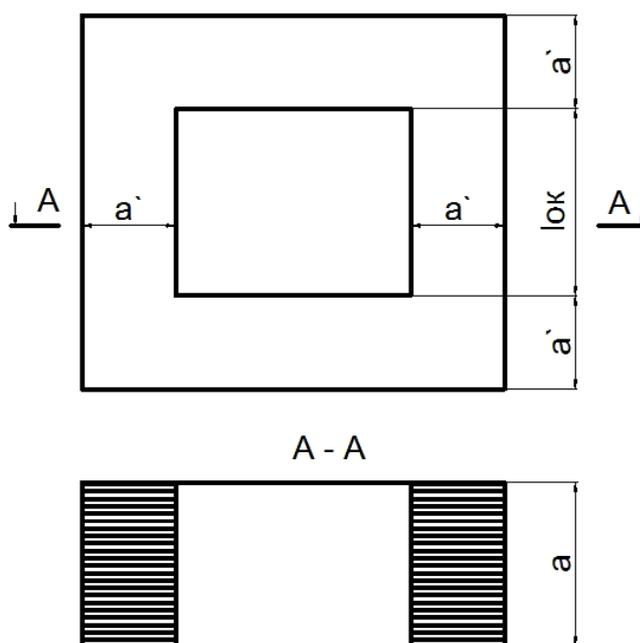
Магнитопровод сварочного трансформатора
